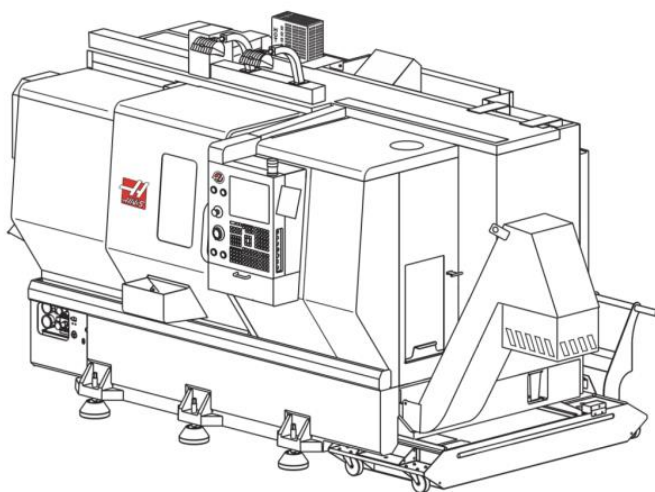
Токарно-фрезерувальний верстат HAAS DS-30Y [25]
